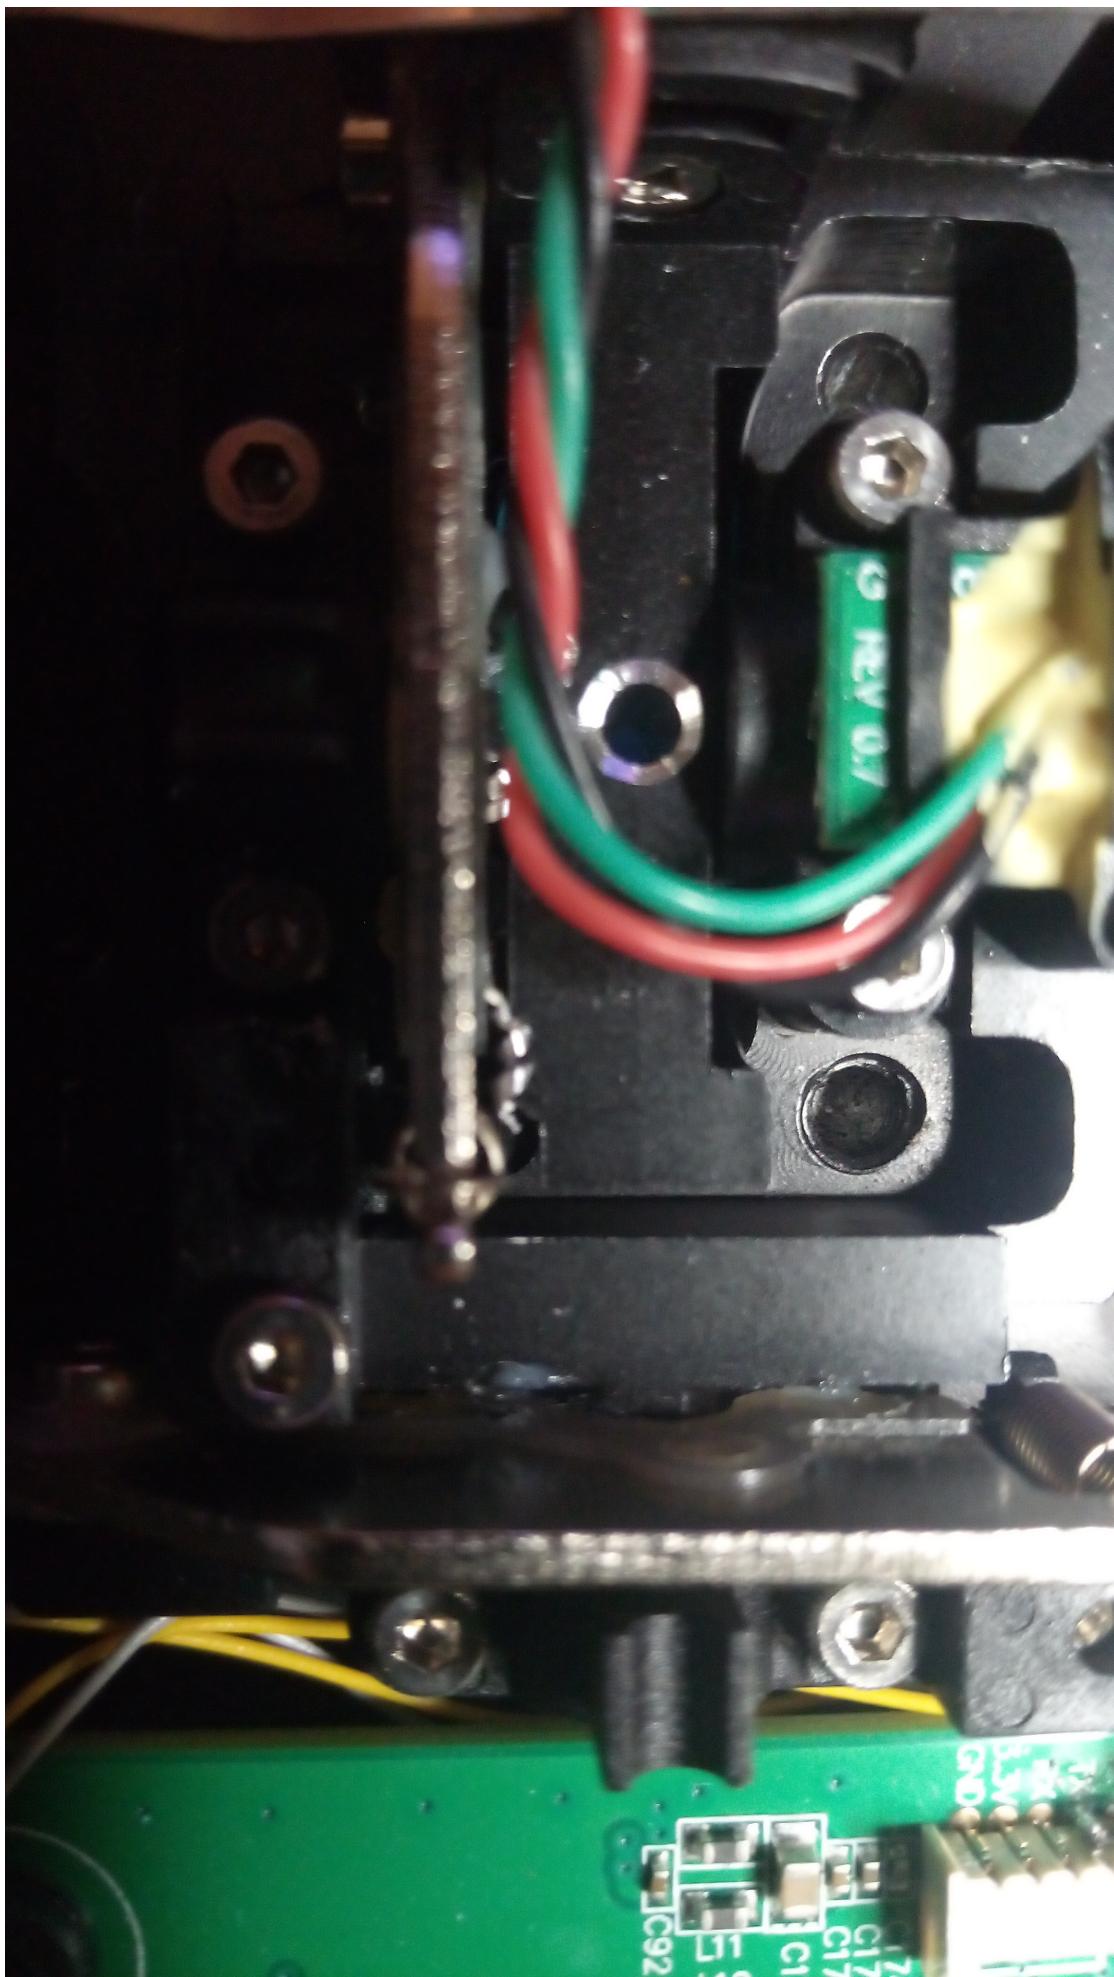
Beginn der Aufbohrung des Knüppelaggregats auf 3,5mm
